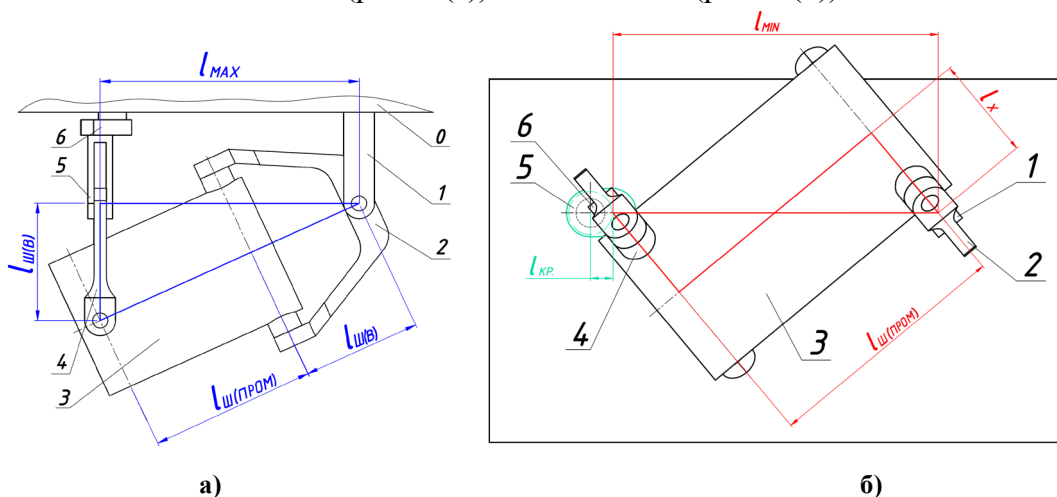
Розроблена галтувальна машина: а – вид зверху, б – вид спереду
